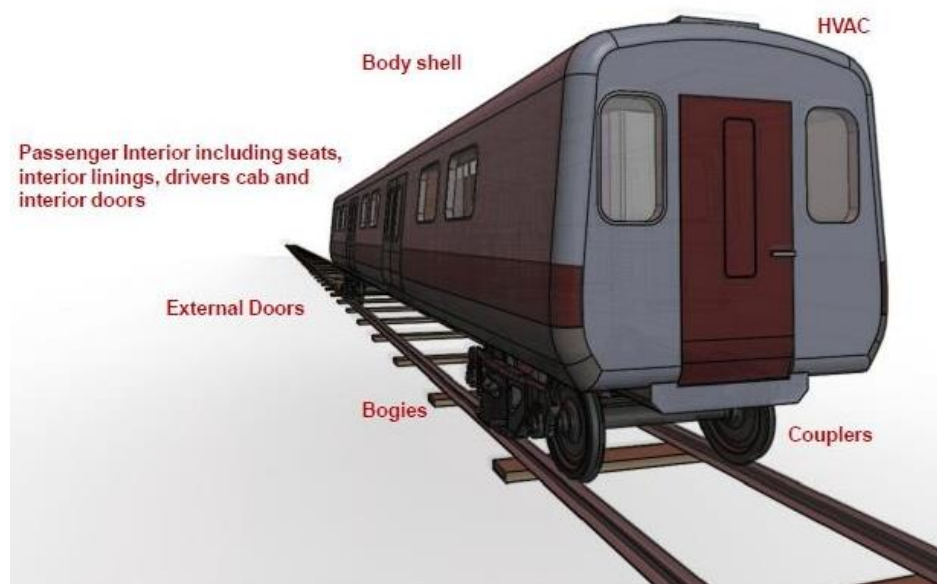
Елементи вагону, які виготовляють з композитних матеріалів, задля зменшення ваги [11].
